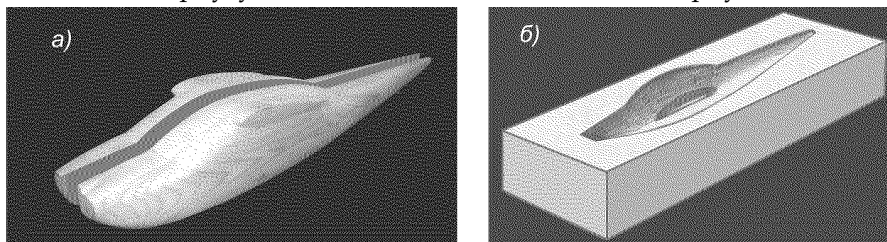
Складена болванка фюзеляжу авіамоделі а – болванка, складена з двох напівболванок; б – гіпсова форма, виготовлена з однієї напівболванки
